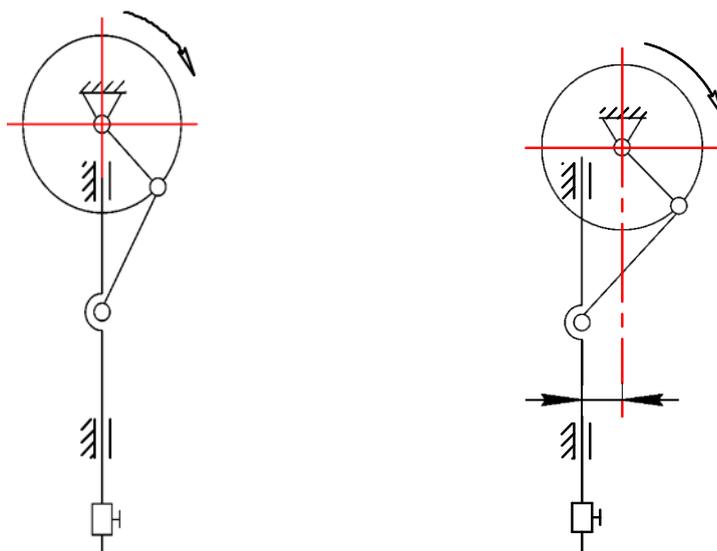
,2. 1-Аксиальный кривошипно-ползунный механизм иглы.
